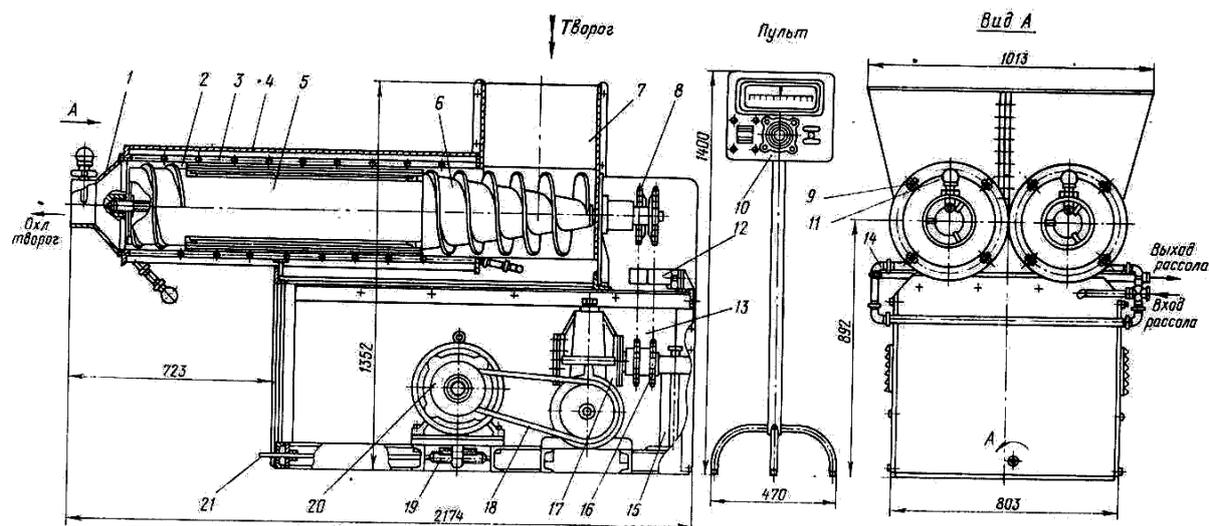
Общий вид охладителя творога двухцилиндрового марки ОТД:
